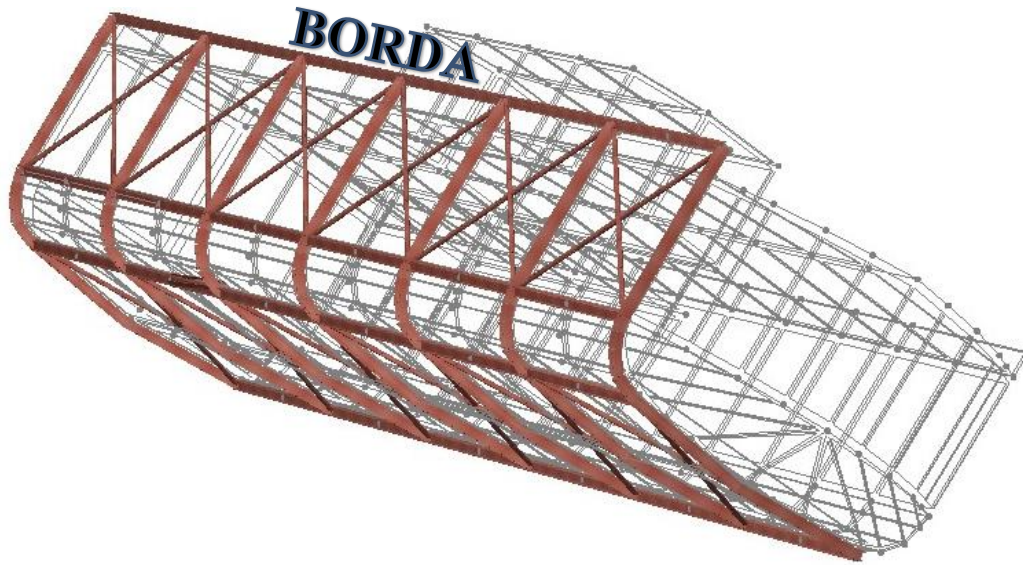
Vista de estructura de RAM Poderoso completo.
